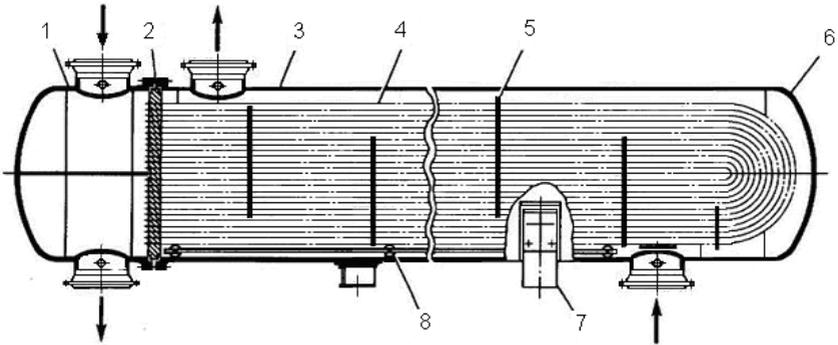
Двухходовой КТТ с U – образными трубами
